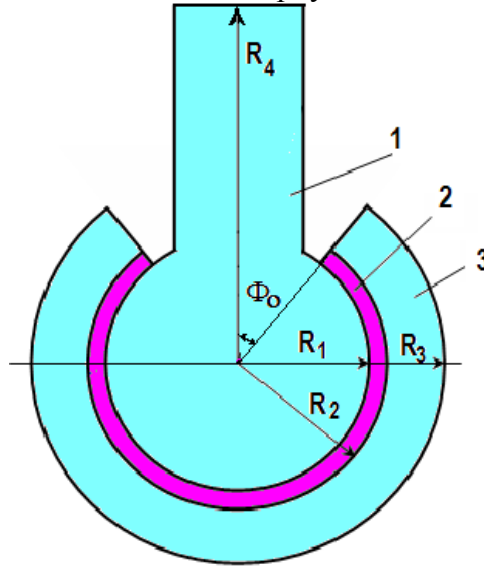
Схема шаровой опоры: 1 – палец; 2 – антифрикционный вкладыш; 3 – корпус
